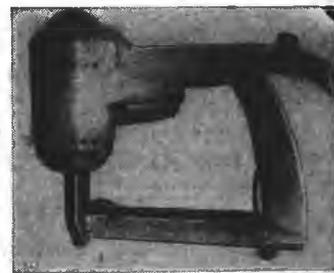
Пневматический молоток для забивки скоб при обивке мягкой мебели
